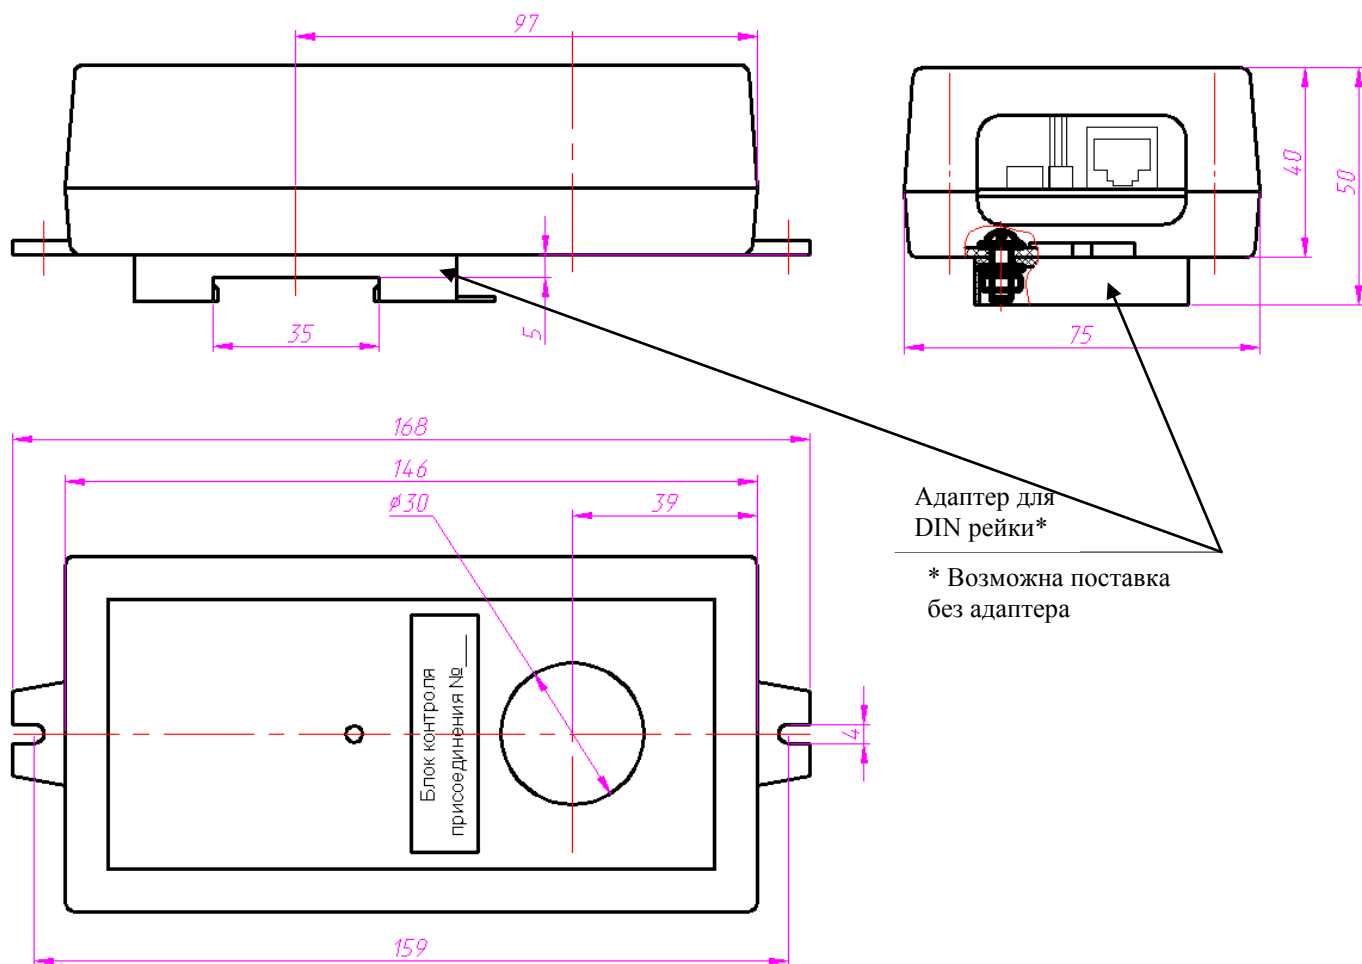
Габаритные и установочные размеры блока контроля присоединения комплекса. Масса блока 0,5 кг.
